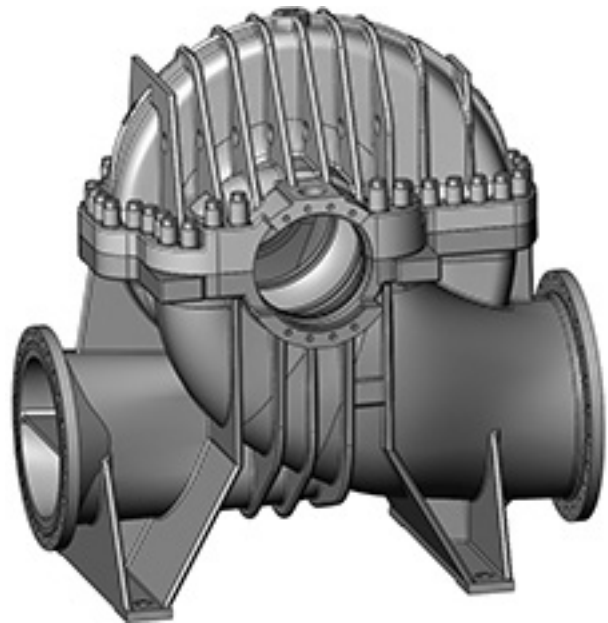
Геометрическая модель базовой конструкции корпуса насоса, вариант 1 (9-5)
